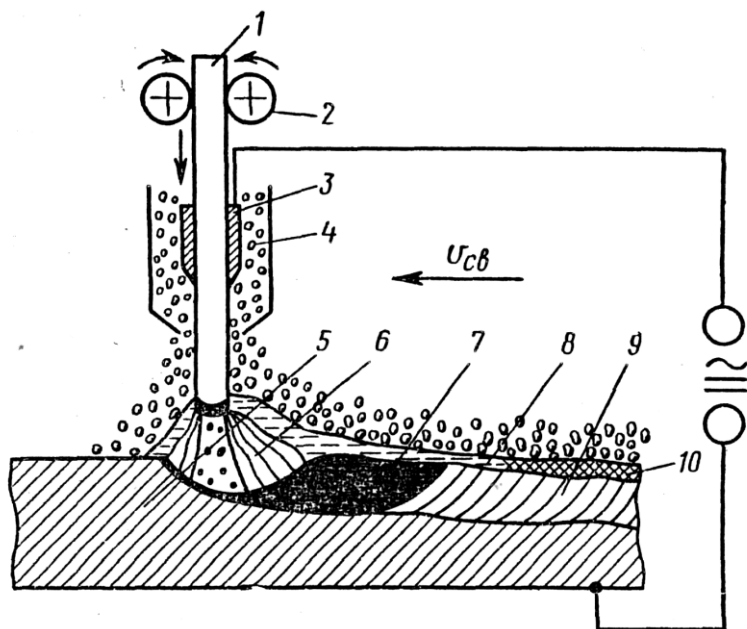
Схема автоматической сварки под флюсом:
